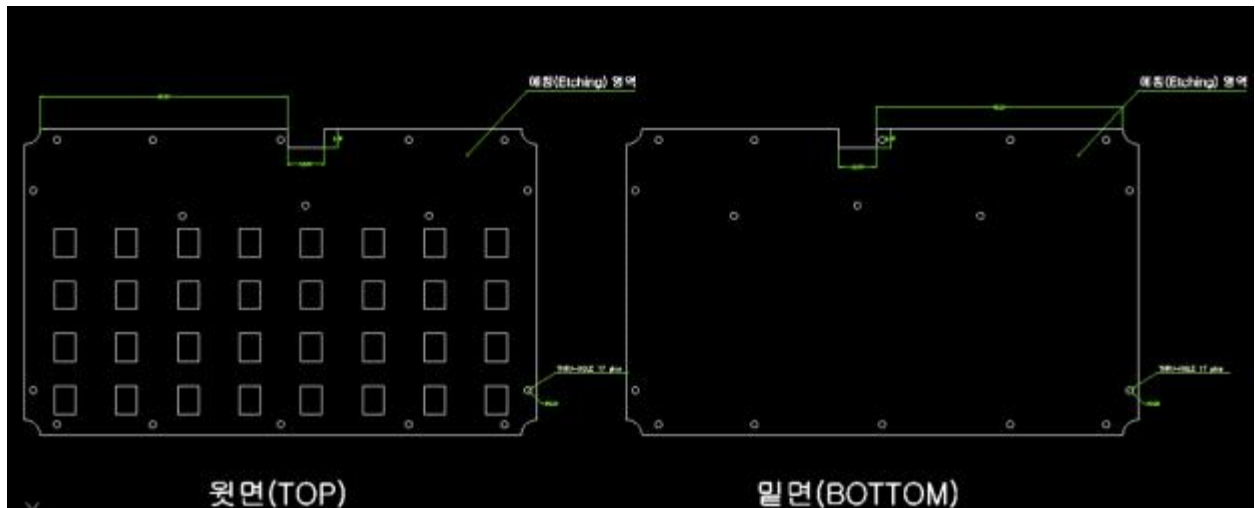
Aperture-Coupled Stacked 8x4 패치 배열 안테나 PCB 도면(복사면)
